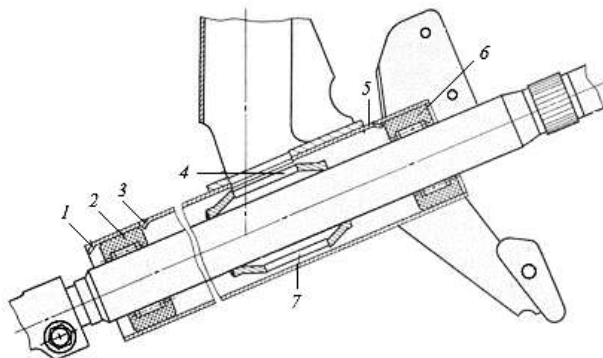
Установка ланки рульового валу на двох плаваючих підшипниках:
